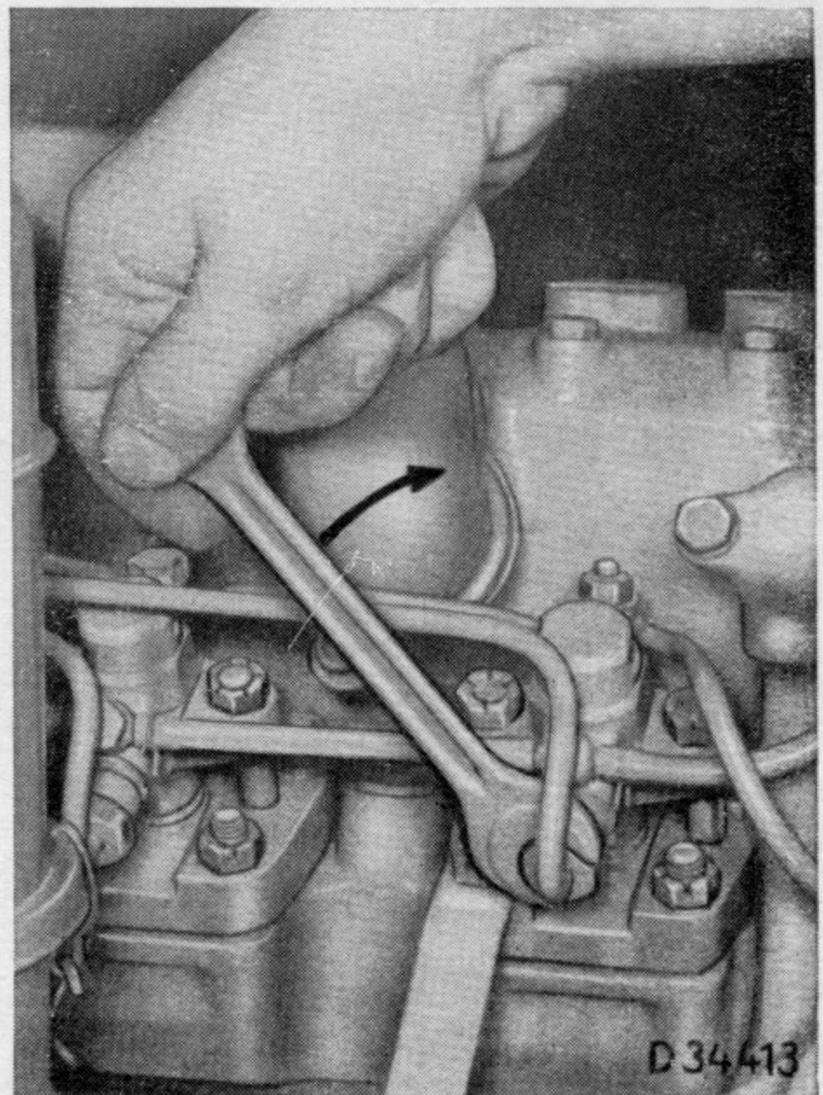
Dichtziehen der Druckrohranschlüsse an den Einspritzdüsen
